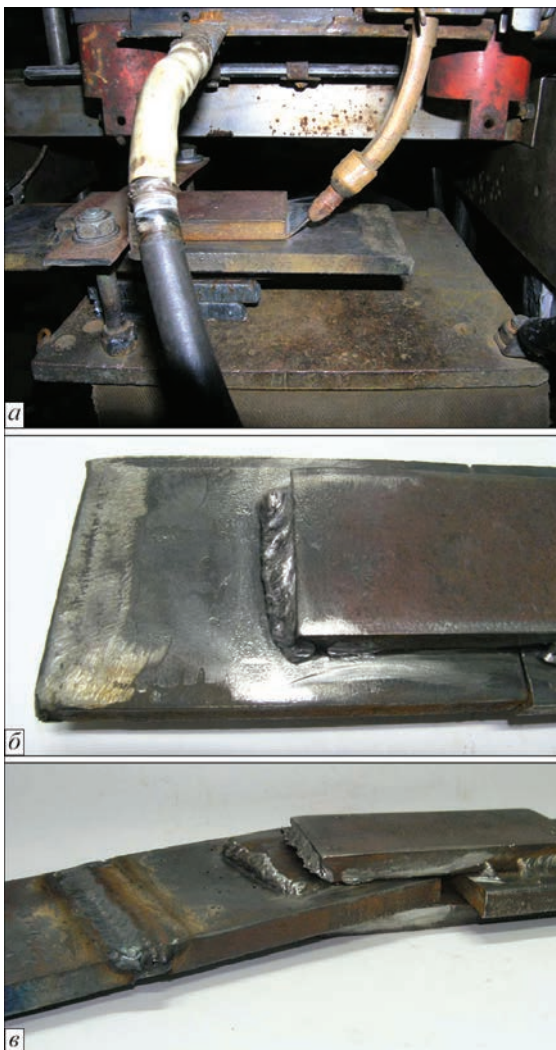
Образец для испытаний на разрыв: перед сваркой (а), после сварки на глубине 200 м (б) и после испытания (в)
